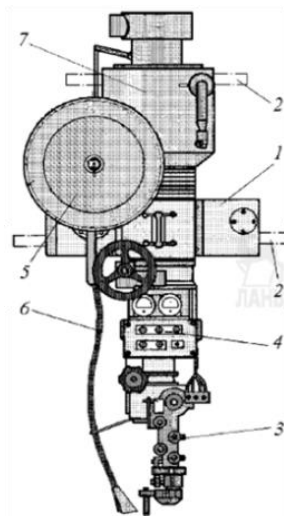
Общий вид подвесного сварочного автомата
